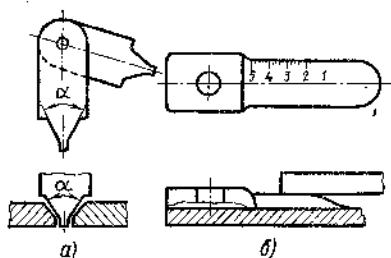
Шаблоны для проверки сборки сварных соединений:
